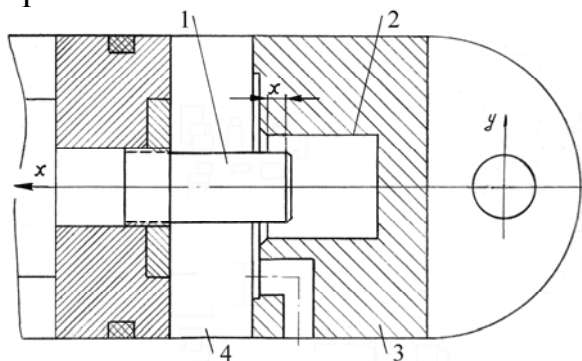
Конструкция поршня, обеспечивающая снижение динамической нагрузки в гидроцилиндре.
